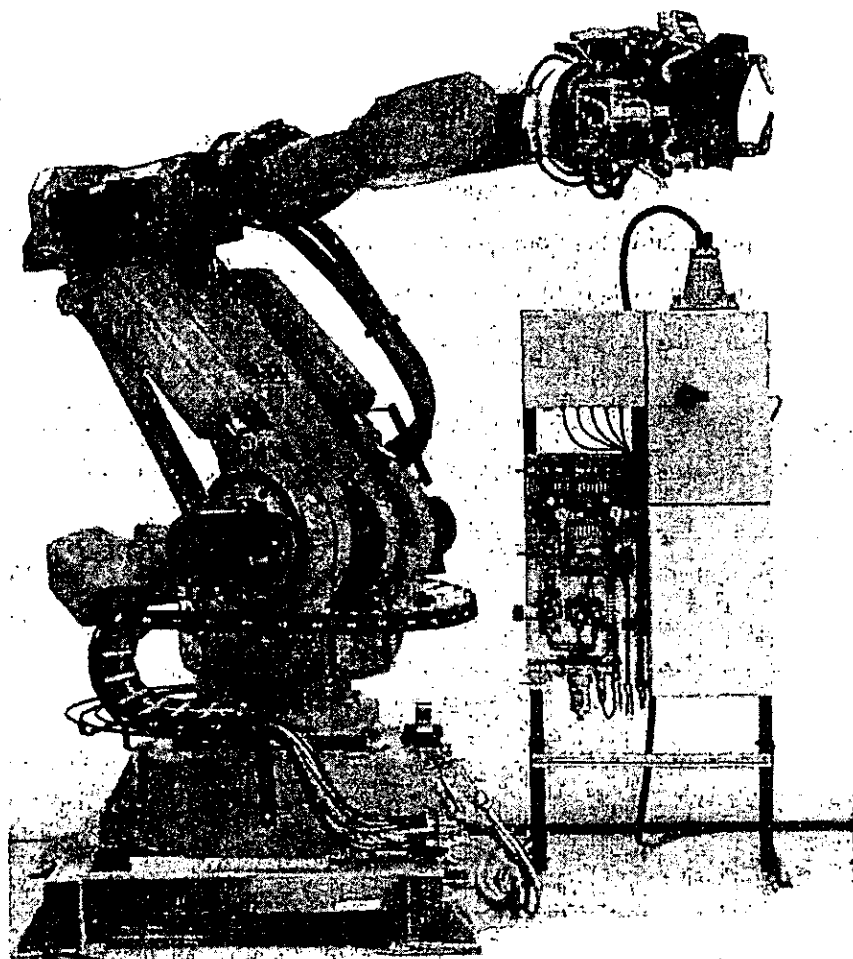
Robot con pistola neumática de soldadura montada en la muñeca.
